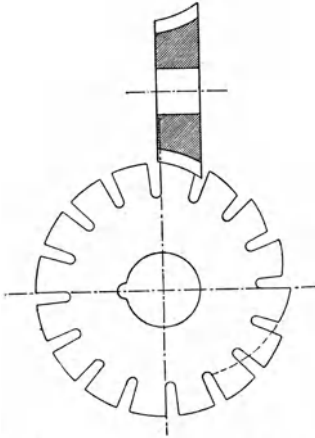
Das Fräsen der Zähne anstatt des Hinterdrehens.
